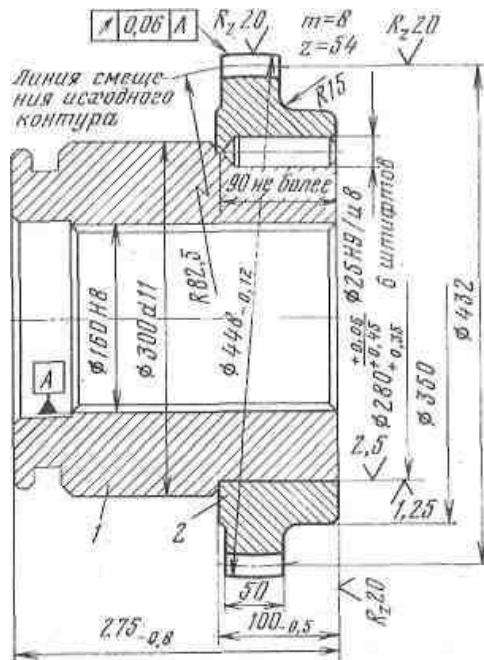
Ремонтный чертеж венца втулки зубчатой муфты экскаватора
